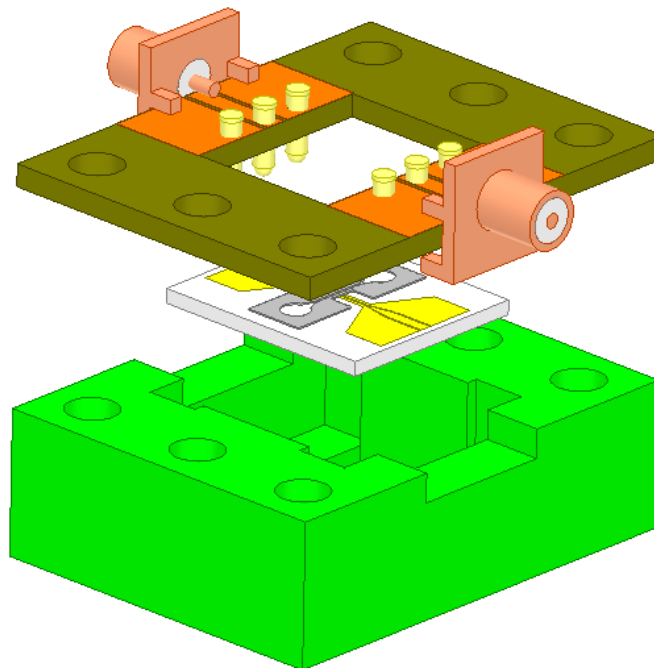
Puce assemblée avec le PCB et le support mécanique
